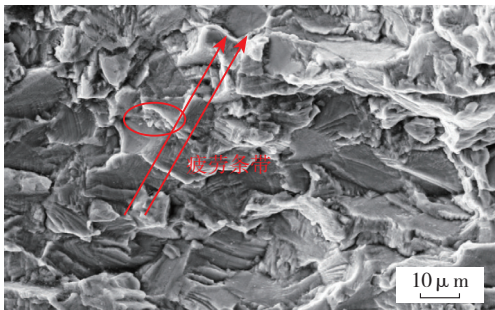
右侧横向裂纹疲劳断口微观形貌
